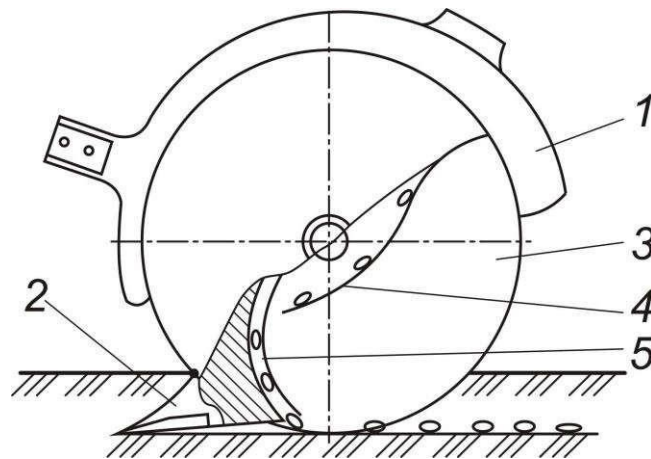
Дисківий сошник зі стабілізатором: 1 – корпус; 2 – розпушувач; 3 – диск; 4 – напрямляч; 5 – ребро
